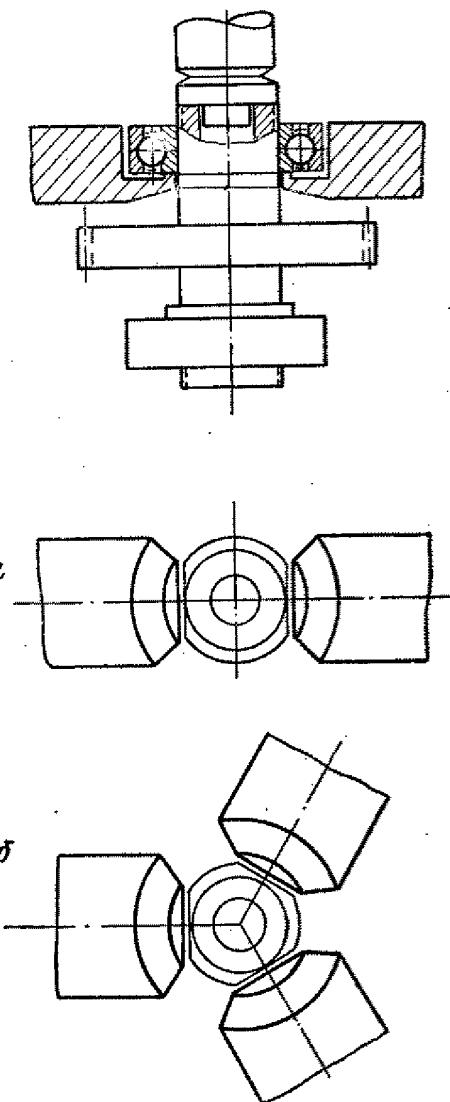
Схема демонтажа подшипников не-разборного типа с вала с помощью двух-захватного (а) и трехзахватного (б) съемника
